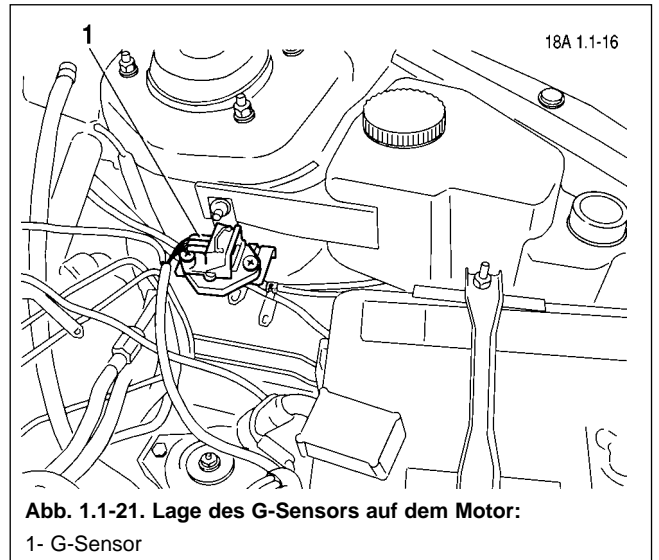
Lage des G-Sensors auf dem Motor:
